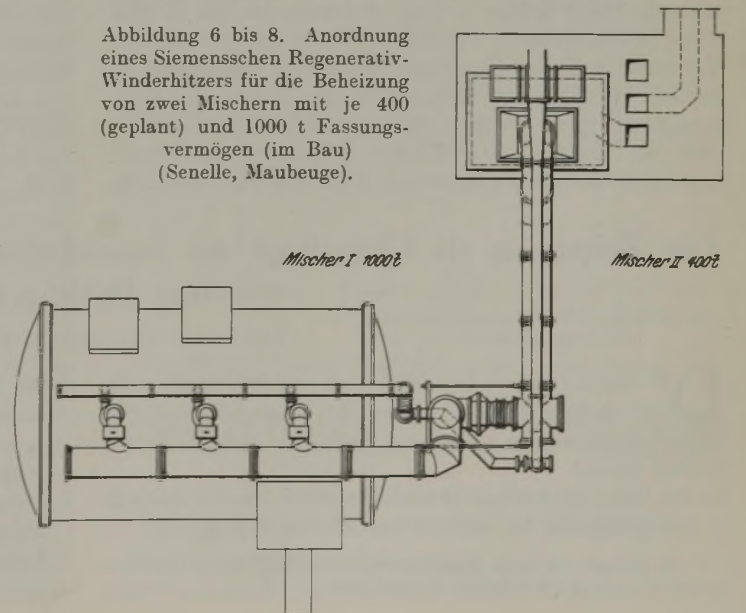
bis 8. Anordnung eines Siemensschen Regenerativ-Wärmerückwärmers für die Beheizung von zwei Mixern mit je 400 (geplant) und 1000 t Fassungsvermögen (im Bau) (Senelle, Maubeuge).
